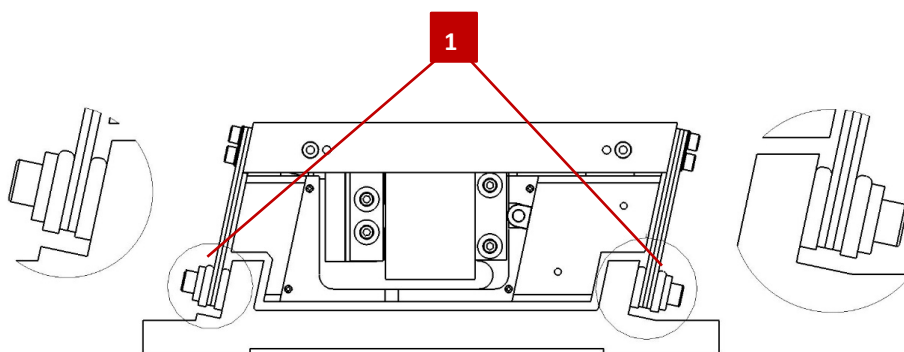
Ensemble de ressorts avec plaques de réglage (1)
